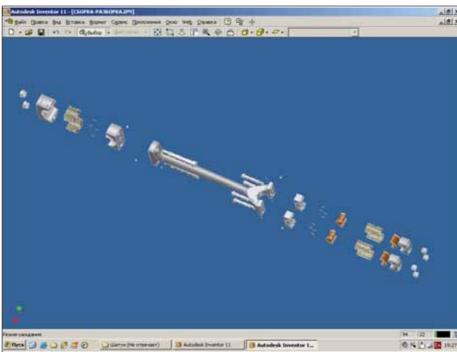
3D-модель сборки-разборки шатуна, выполненная в Autodesk Inventor
